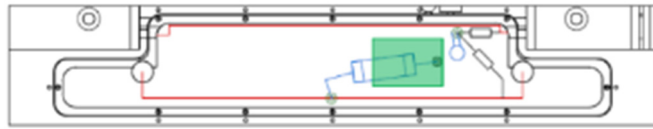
AFAS-B Top Fork 及び Bottom Fork 検出器のアンプ配置図
